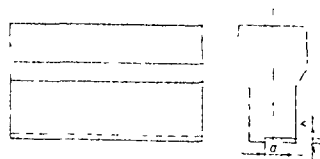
Доработка поддержек 54389-11 групповых штампов для клепки заклепок с плоско-выпуклыми головками
